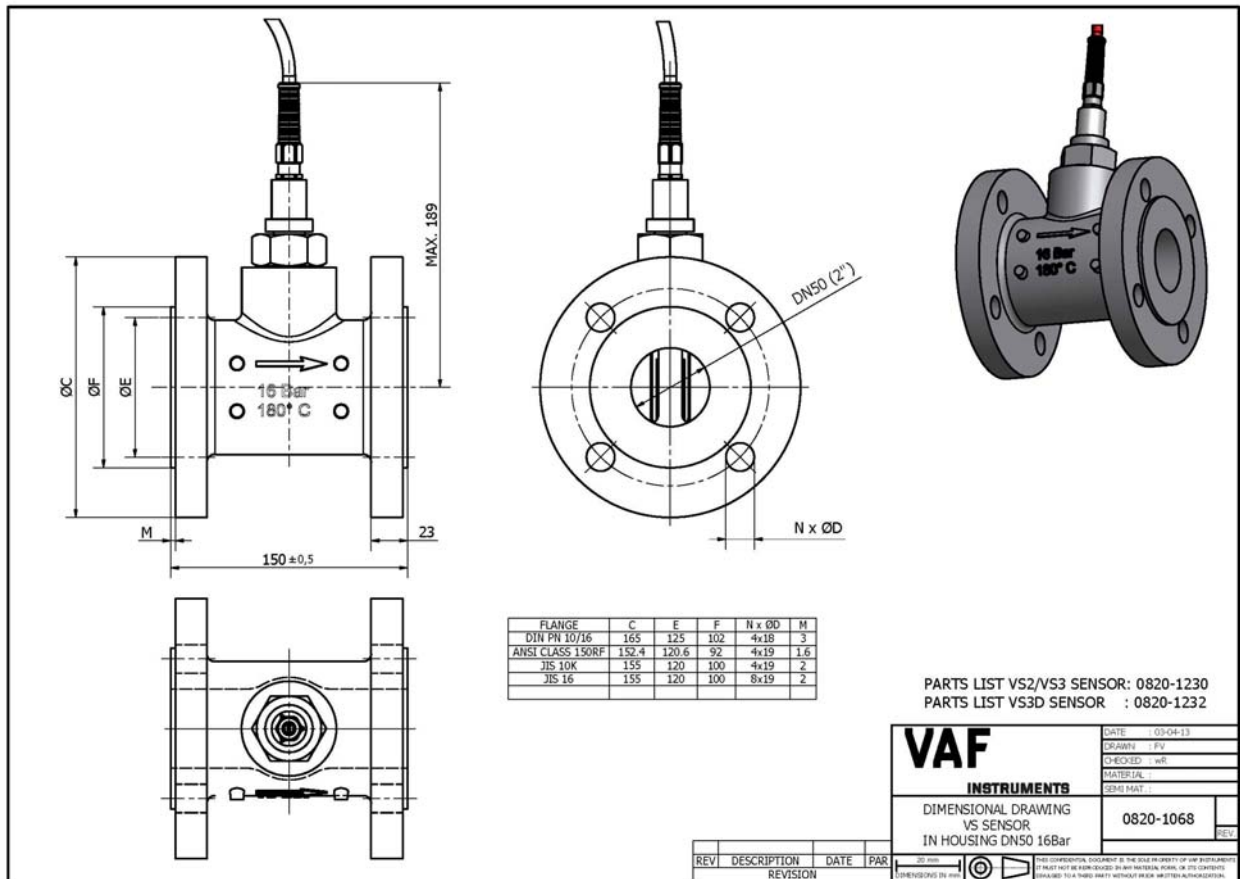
Dimensões do sensor ViscoSense<sup>®</sup>3 ( todas as dimensões em milímetros)
